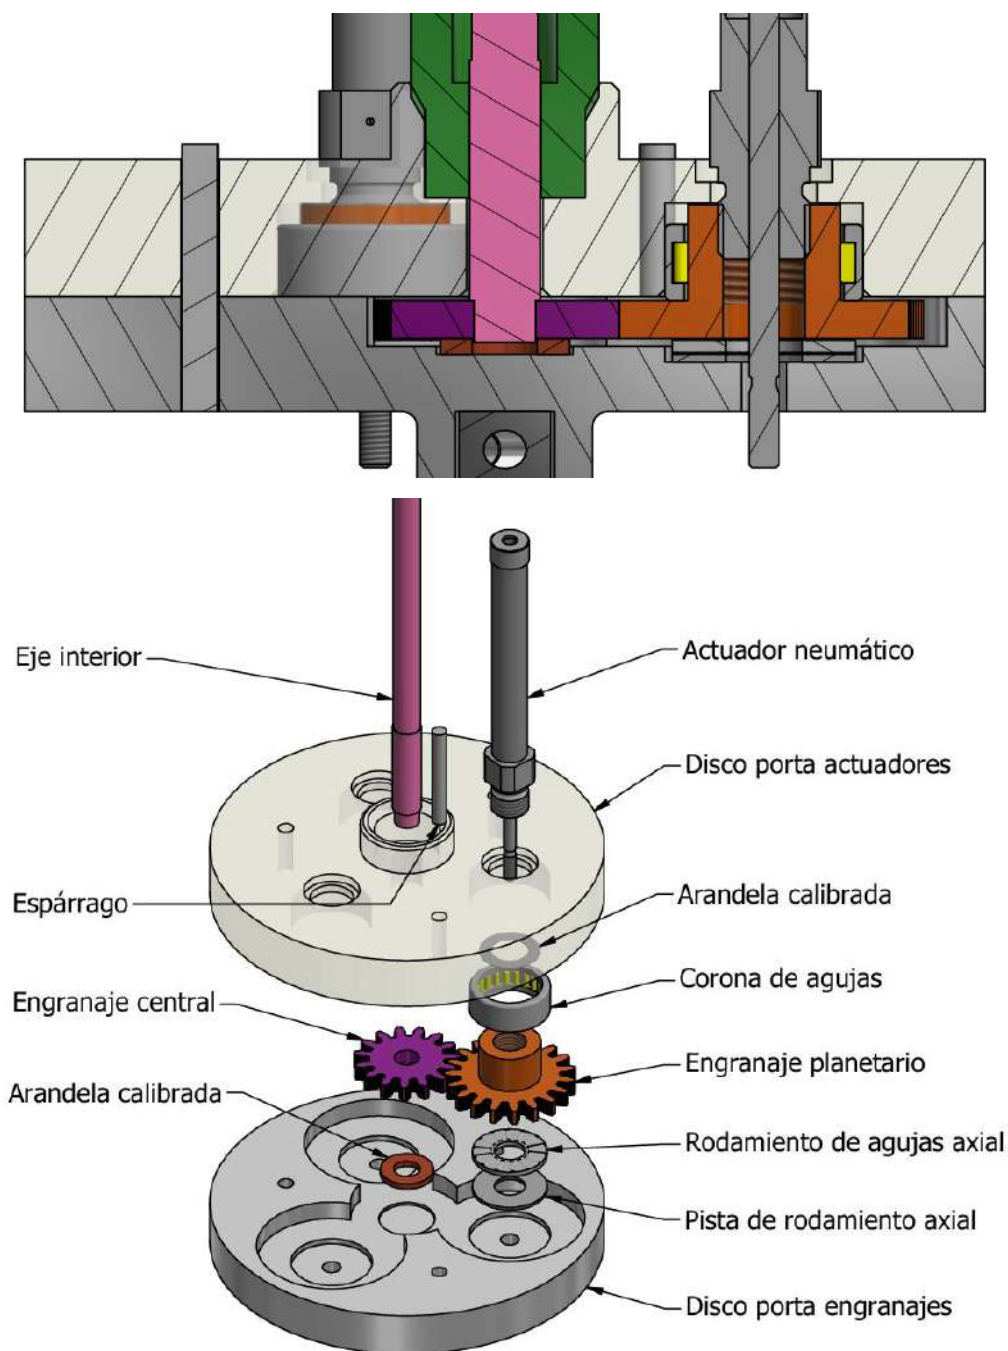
Vista explotada y en corte del conjunto cabezal
